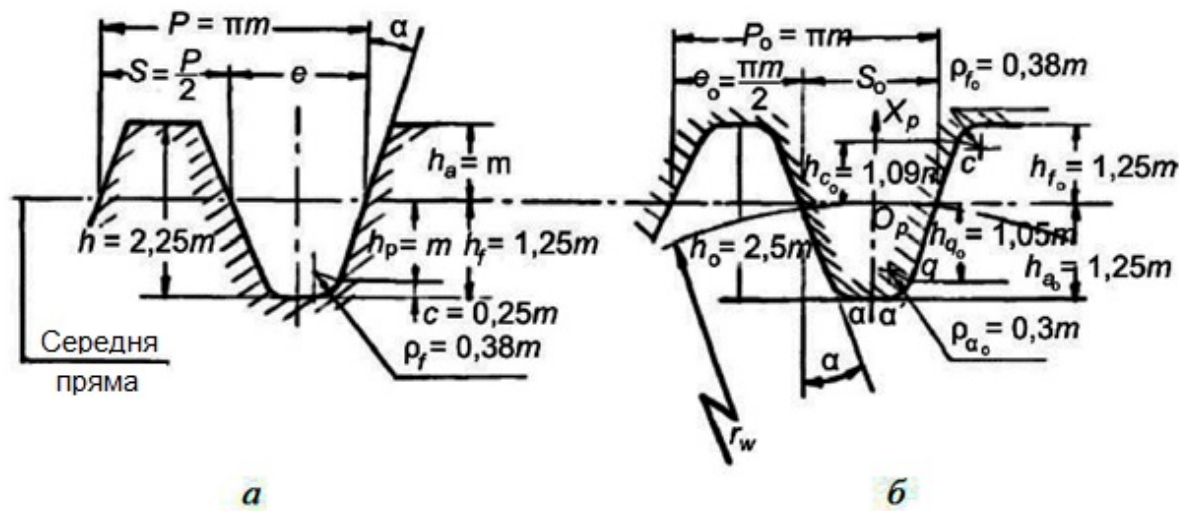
Вихідний контур рейки: *a* – для зубчастих коліс; *б* – для інструментів
